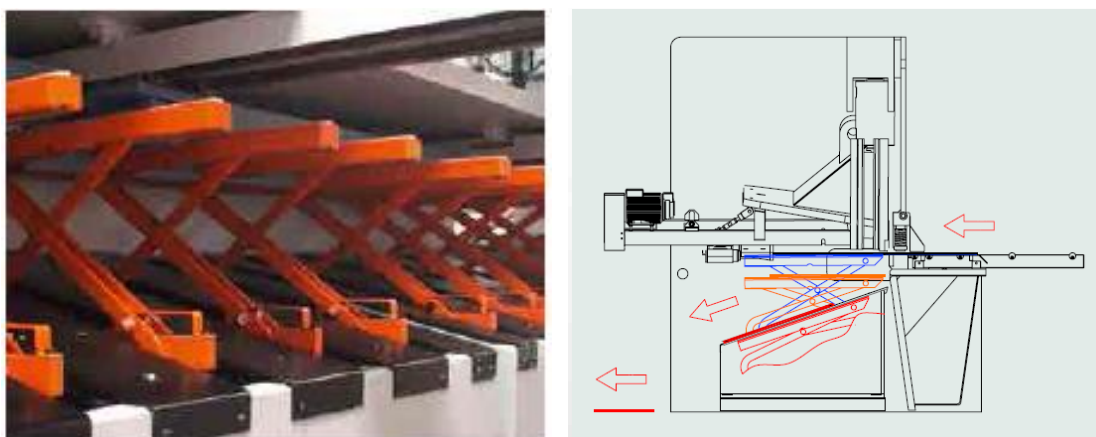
Sistema de apoio de chapa fina do fabricante Ermaksan (Ermaksan, 2014)
